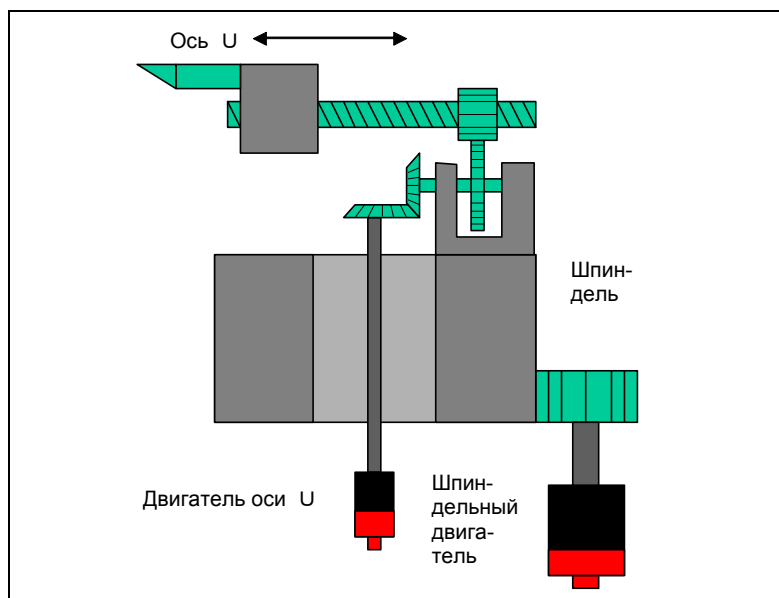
(b) Пример конструкции станка с осью U
